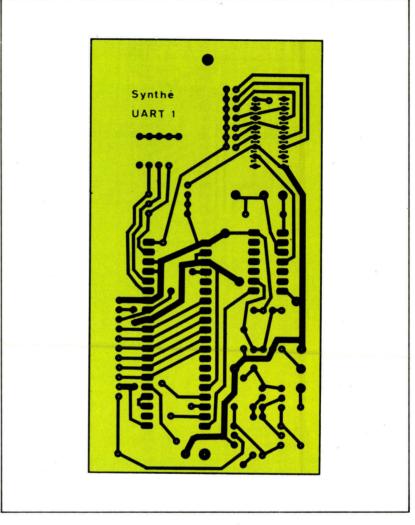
Circuit imprimé vu côté « soudures ».
